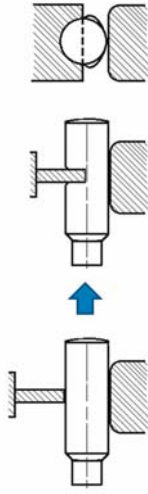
Схема процесу вдавлювання вузького бойка в заготовку
